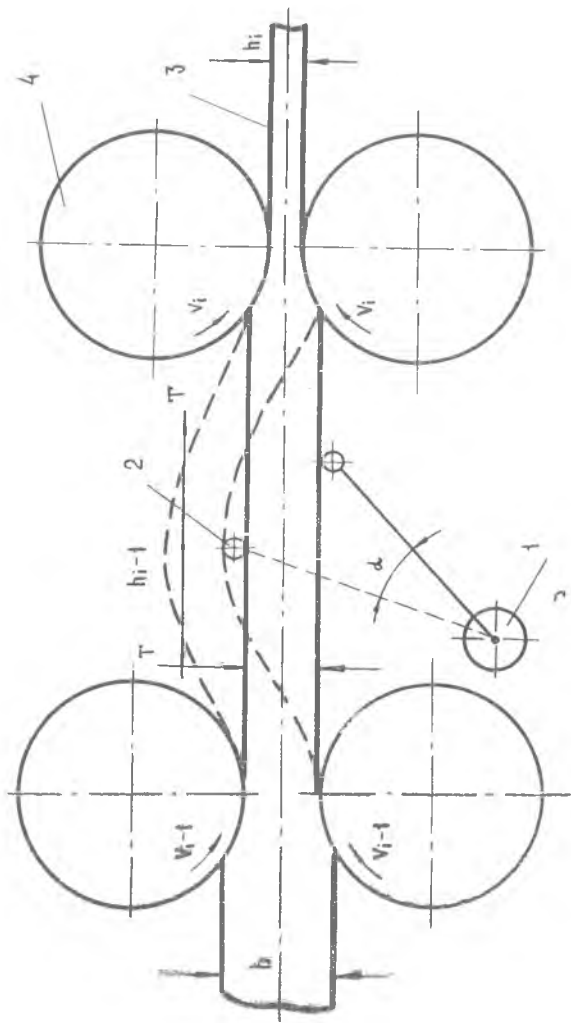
Схема работы петледержателя: 1 — двигатель петледержателя; 2 — ролик петледержателя; 3 — прокатываемая полоса; 4 — рабочие вальки
